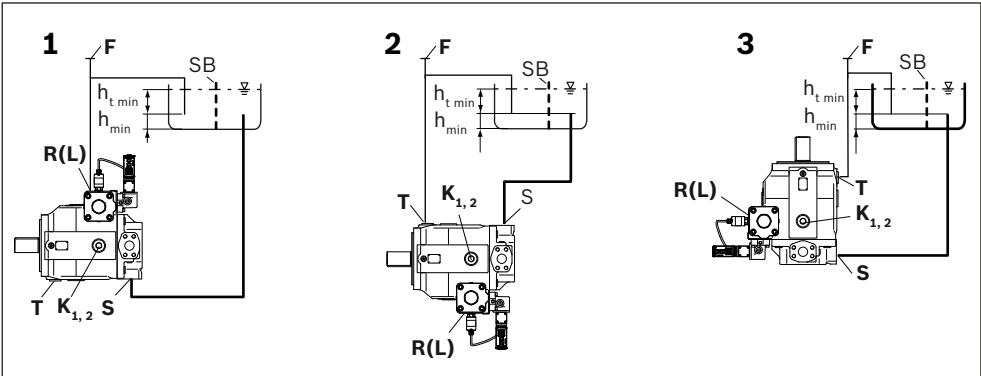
Untertankeinbau A4VSO mit Einbaulage 1–3
